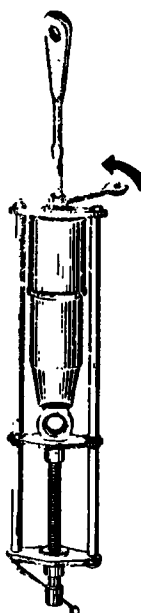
Разборка переднего амортизатора при помощи приспособления.
